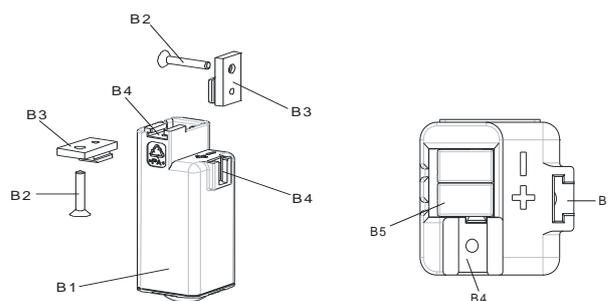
Wand- oder Deckenmontage mit Hilfe eines Klemmstückes
